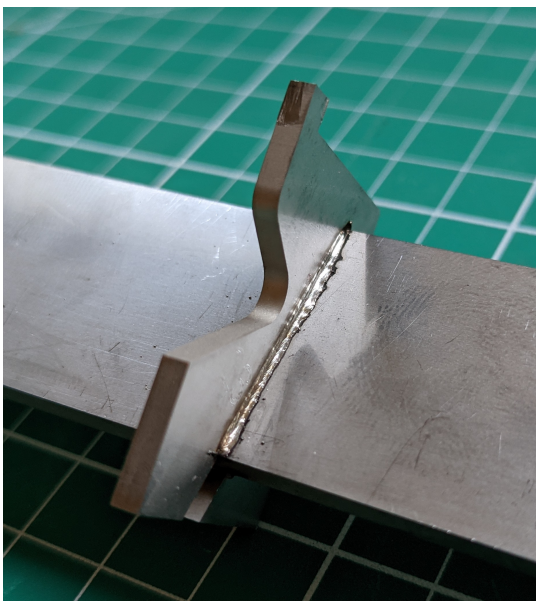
Vue du talon soudé sur une des aubes.
